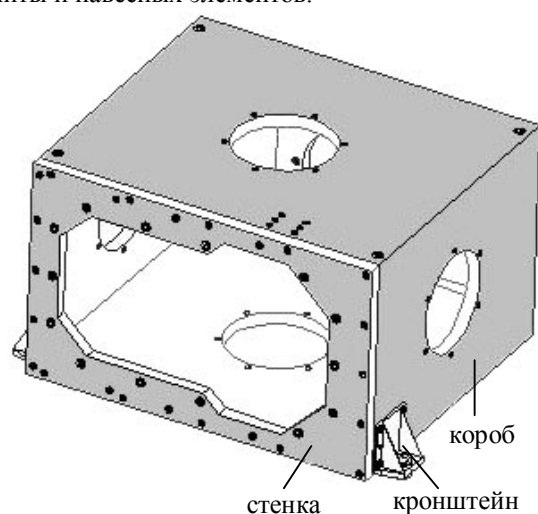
Схема корпуса сканера высокой разрешающей способности
